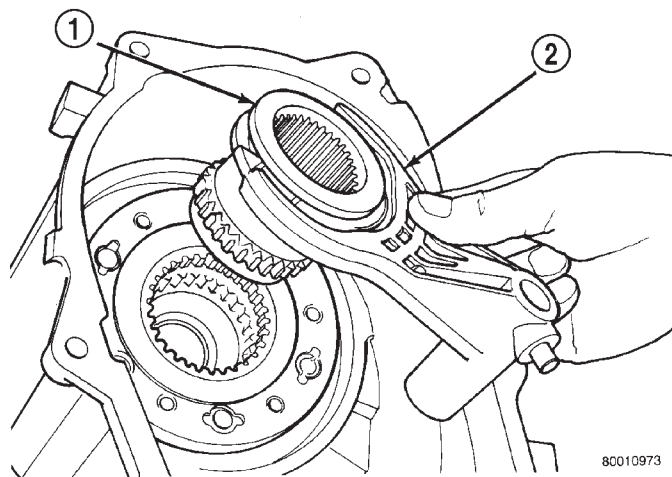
Desmontaje de la horquilla y manguito de escala de posiciones
